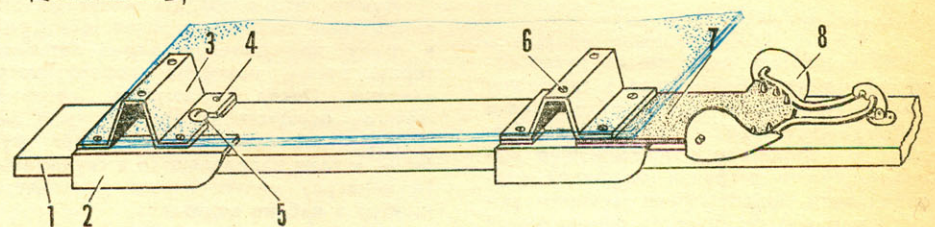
Узлы крепления корпуса прогулочного компромисса:
